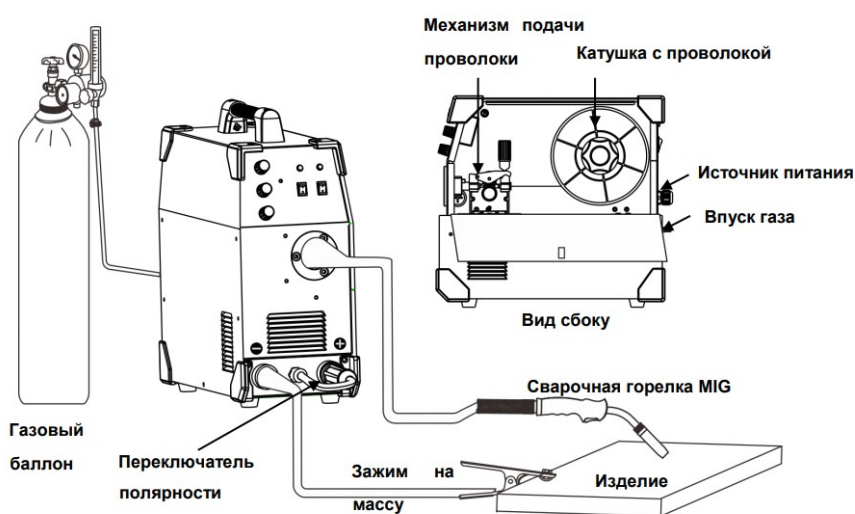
Комплект полуавтоматического сварочного аппарата
